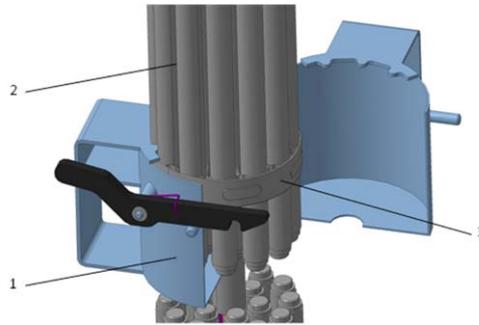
Установка чашки на ДР верхнего ПТ: 1 – чашка; 2 – верхний пучок твэлов; 3 – ДР 11
